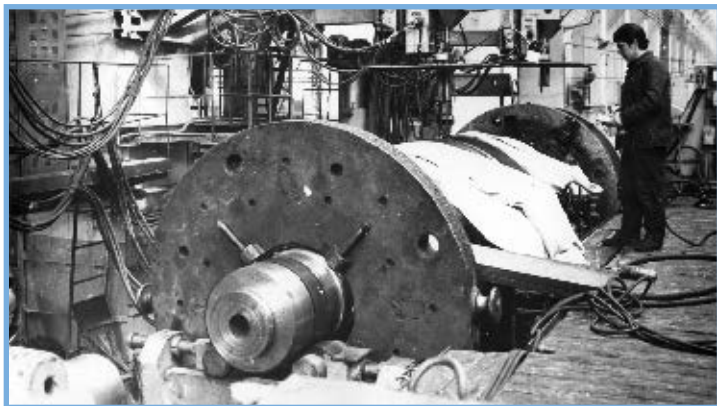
Сварка ротора ЦНД турбины К-300-240 мощностью 300 МВт для ТЭС
